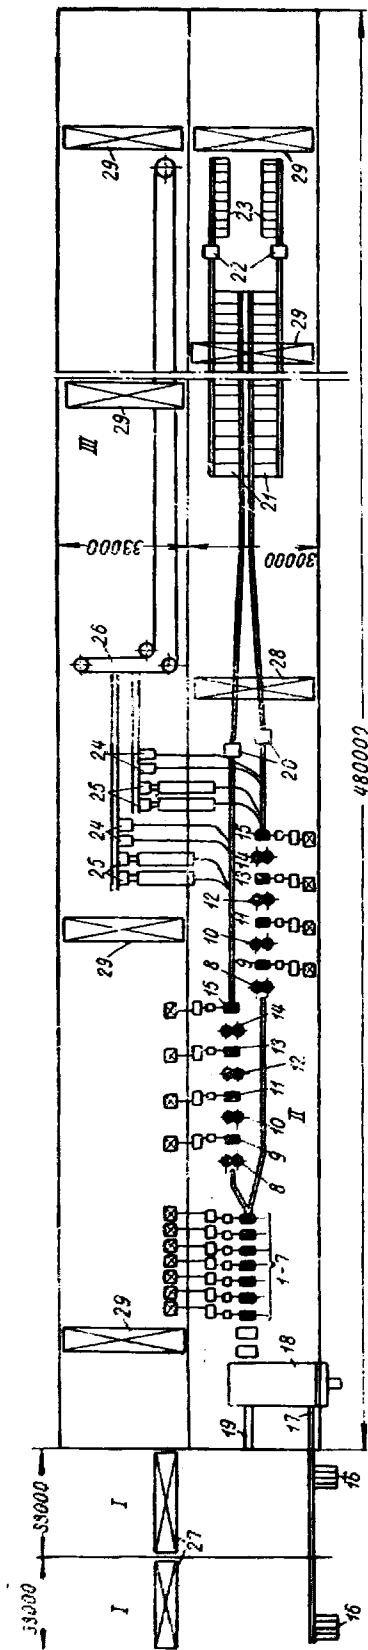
Схема расположения оборудования непрерывного мелкосортного стана 250:
